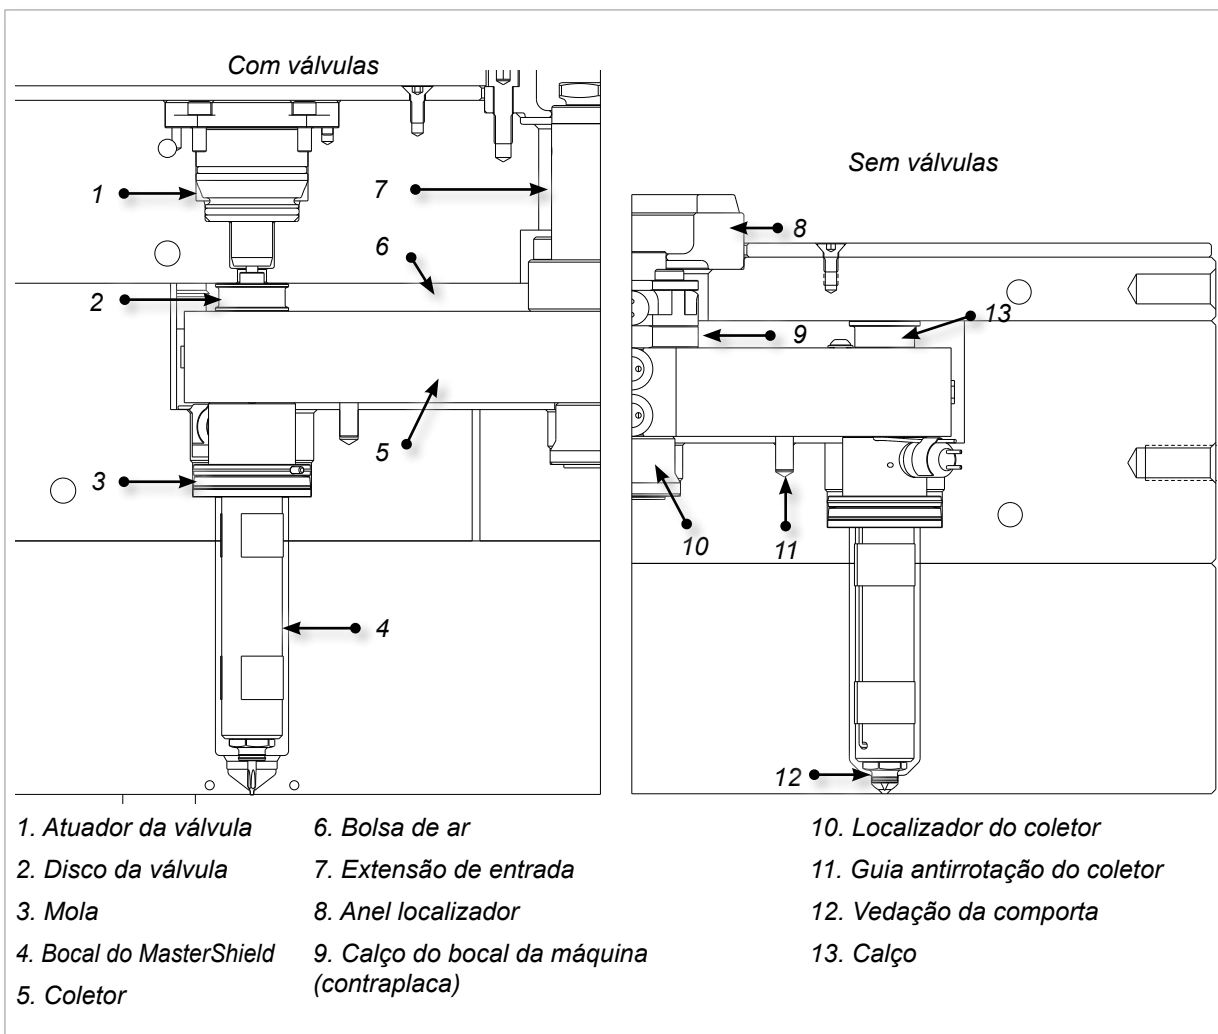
Diagrama de um sistema MasterShield soldado
